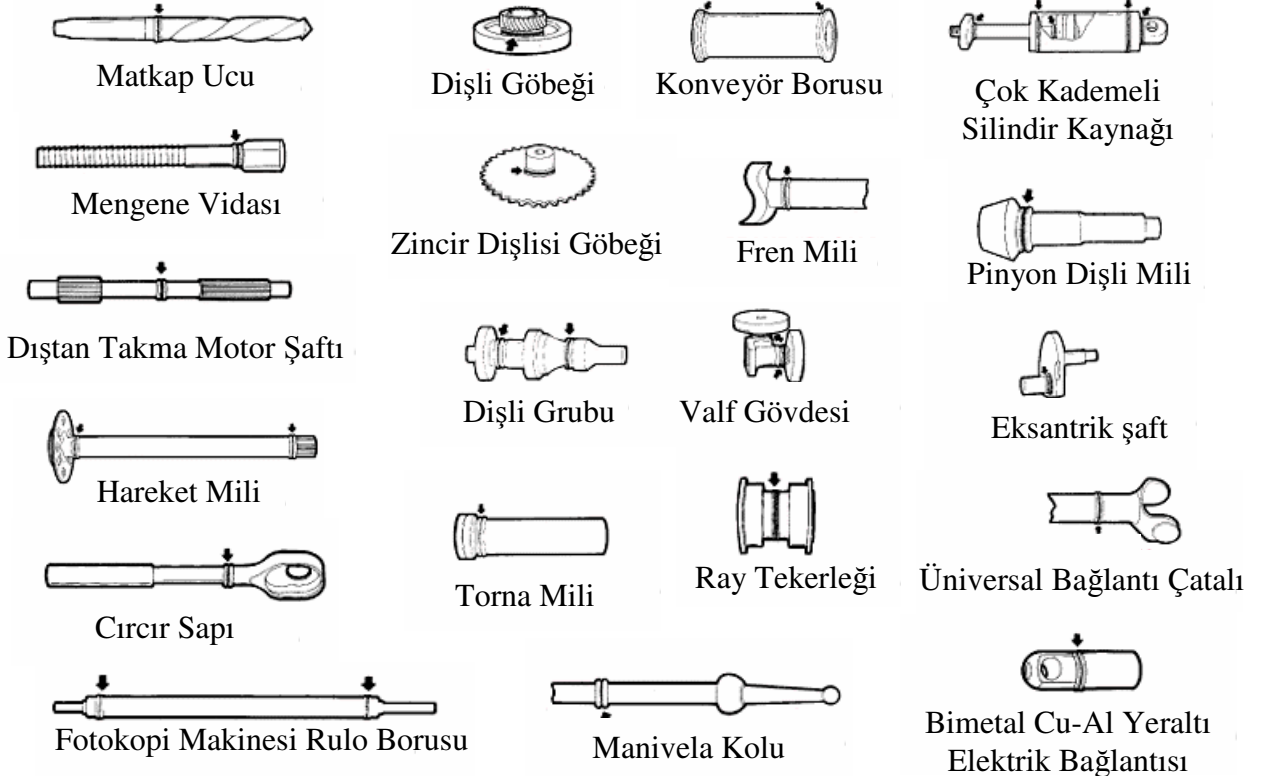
Sürtünme kaynağı ile imal edilmiş parça (www.mtiwelding.com)
